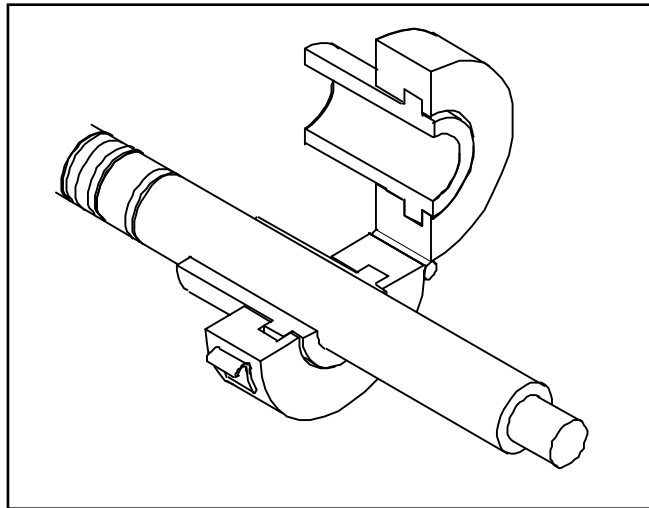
Carcaza y rueda dentada abiertas, con el cable en posición, listo para cerrar y comenzar el trabajo de pelado del cable.
